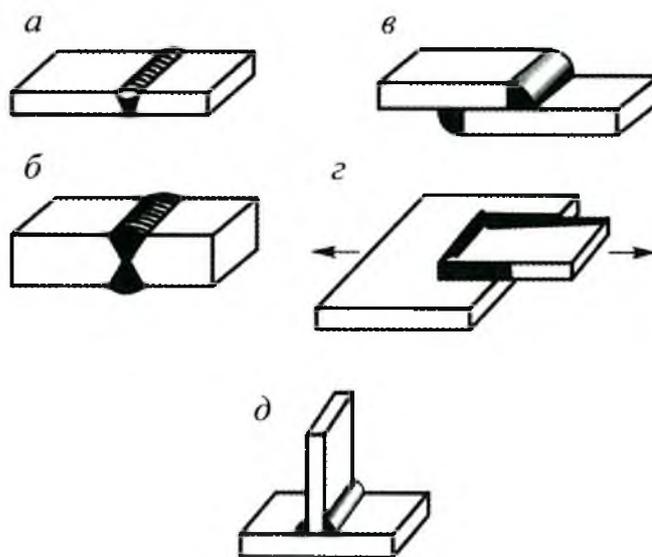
Виды сварных швов: а, б — стыковые; в, з, д — угловые
